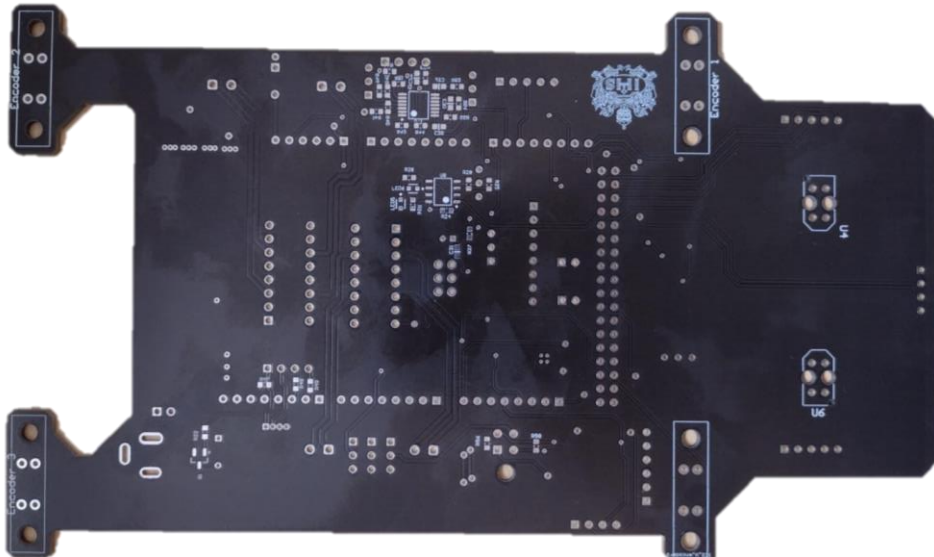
Vista inferior del PCB fabricado versión 3 (Final)
